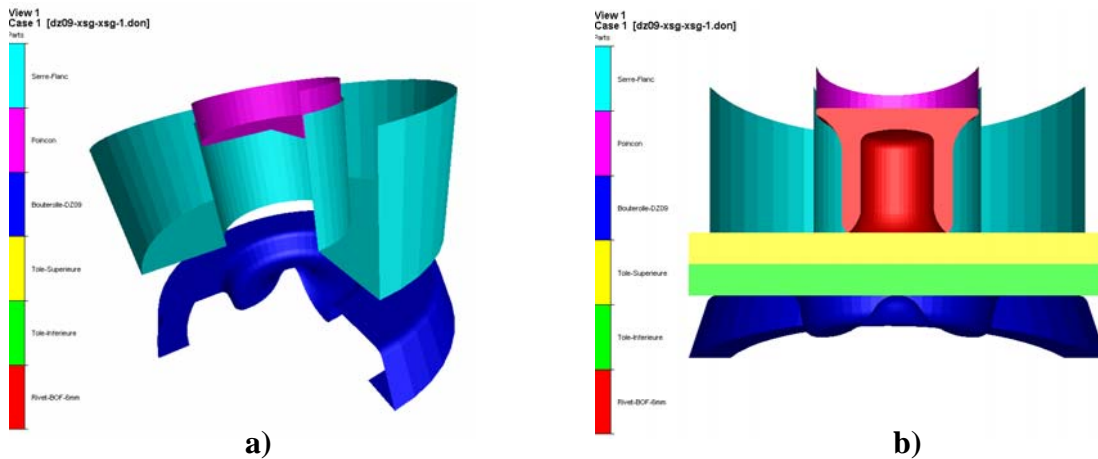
a) outillage seul – b) outillage + rivet et tôles
